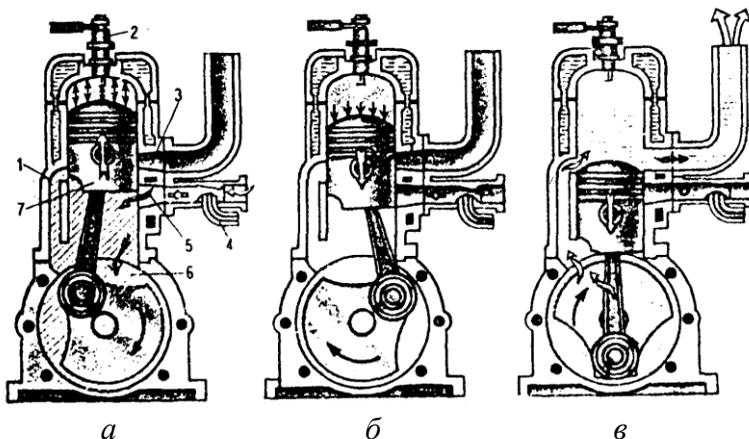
Схема рабочего процесса двухтактного карбюраторного двигателя:
